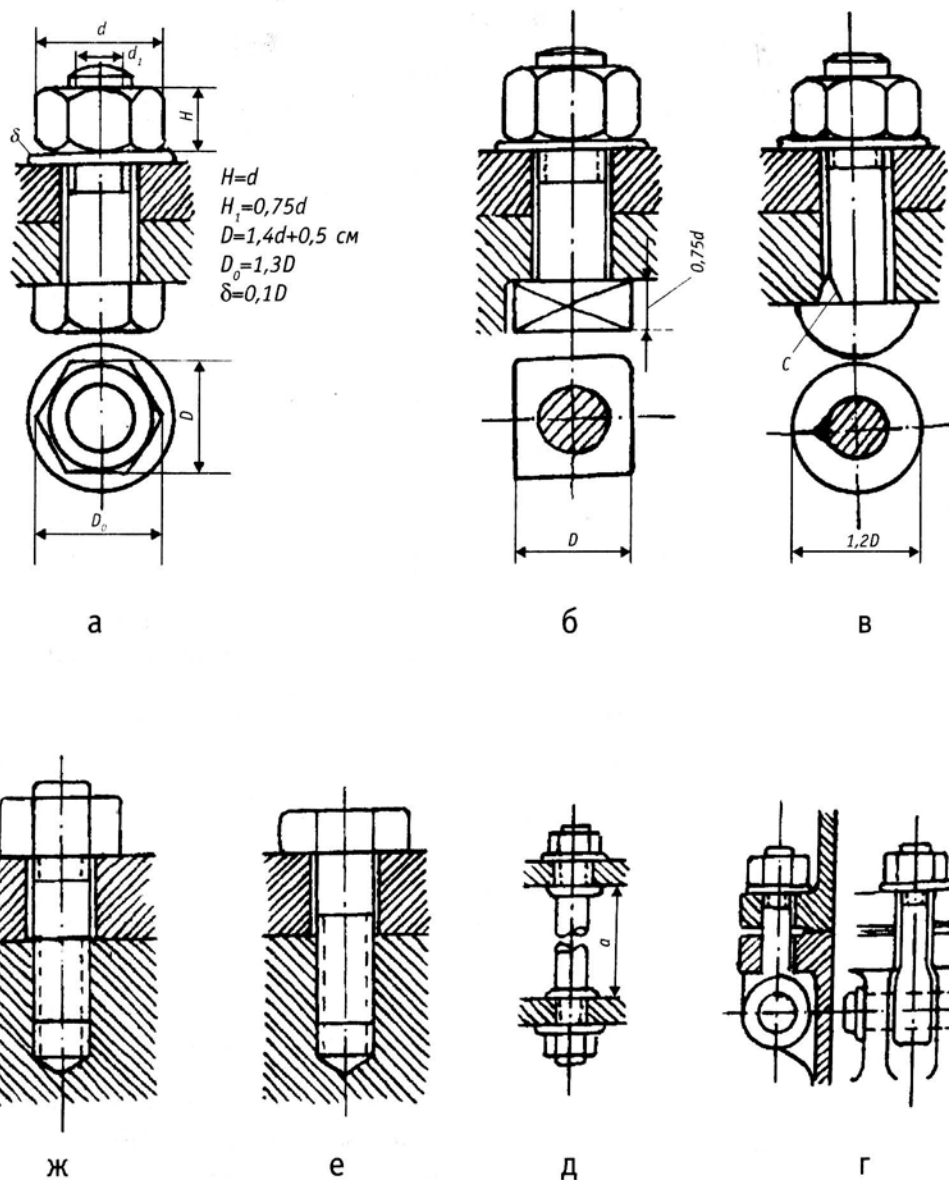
Болты: а — с шестигранной головкой; даны приблизительные соотношения между размерами; б — с квадратной головкой; в — с шаровидной головкой и усом против проворачивания; г — откидной; д — распорный (установочный); е — вкручиваемый (без гайки); ж — шпилечный (шпилька)
